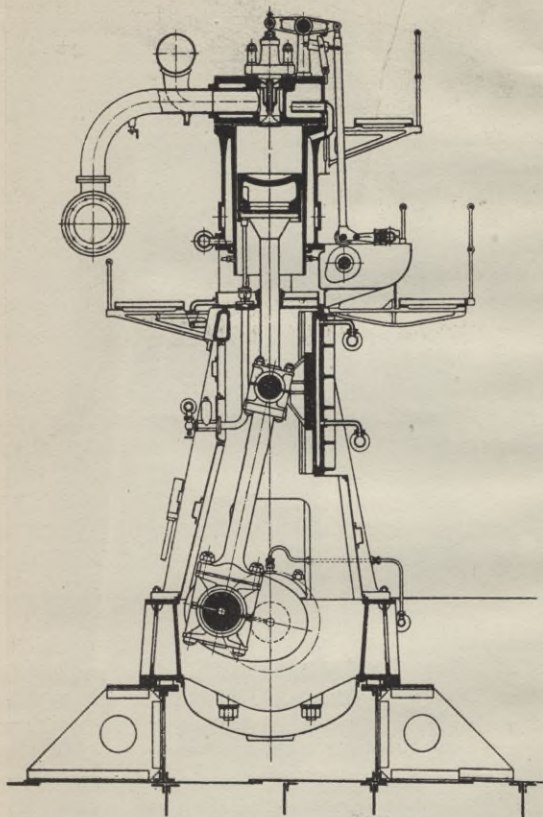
Umsteuerbare Sechszylinder-Viertaktschiffsdieselmachine von Burmeister & Wain. Ausführung der A. E. G. $D = 630$ mm, $s = 960$ mm, $n = 125$ Umdr/Min., $N_i = 1550$ PSi.
